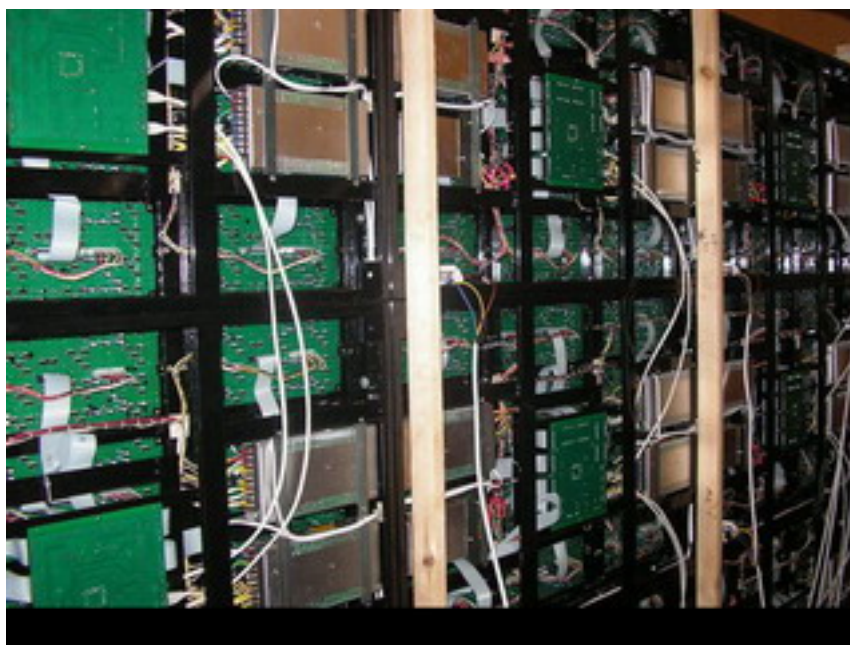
Набірний відеоекран (вид з боку монтажу)
